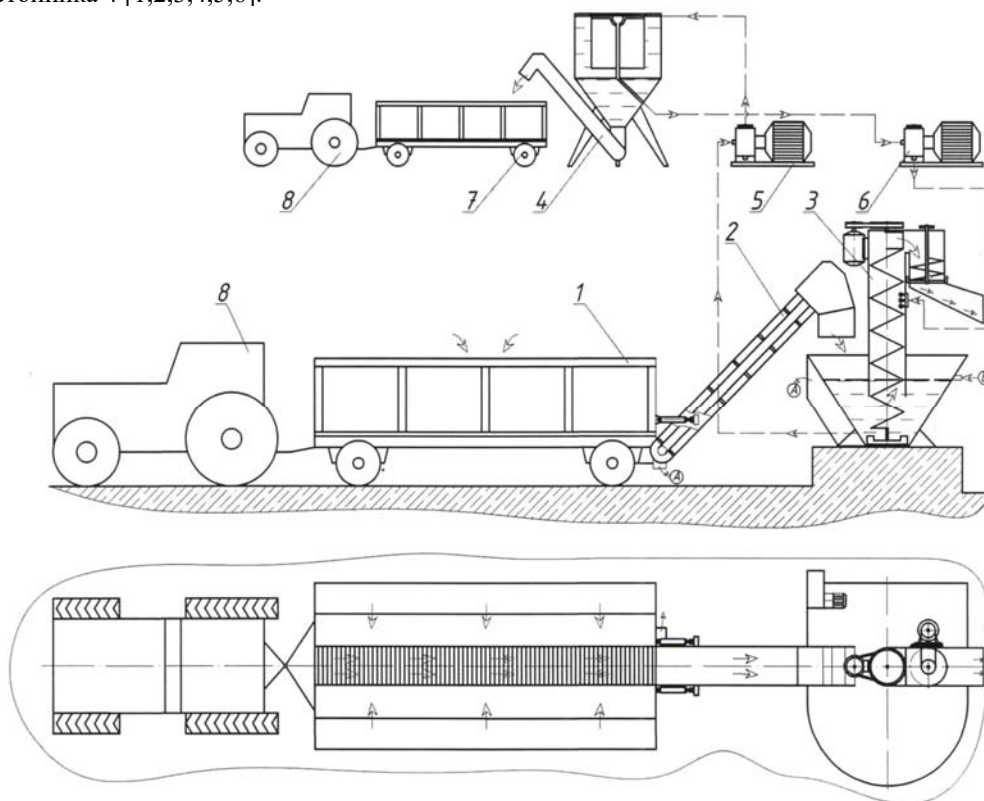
Технологическая схема БТС транспортировки и приготовления корнеплодов:
